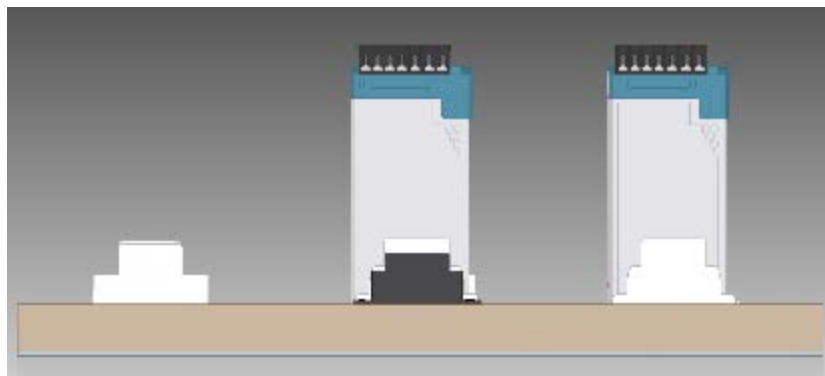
Vista de perfil del modelo 3D de la plancha.
